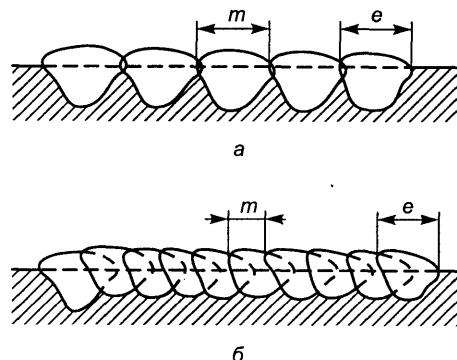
Схема наплавки валиков при разной величине шага наплавки:
